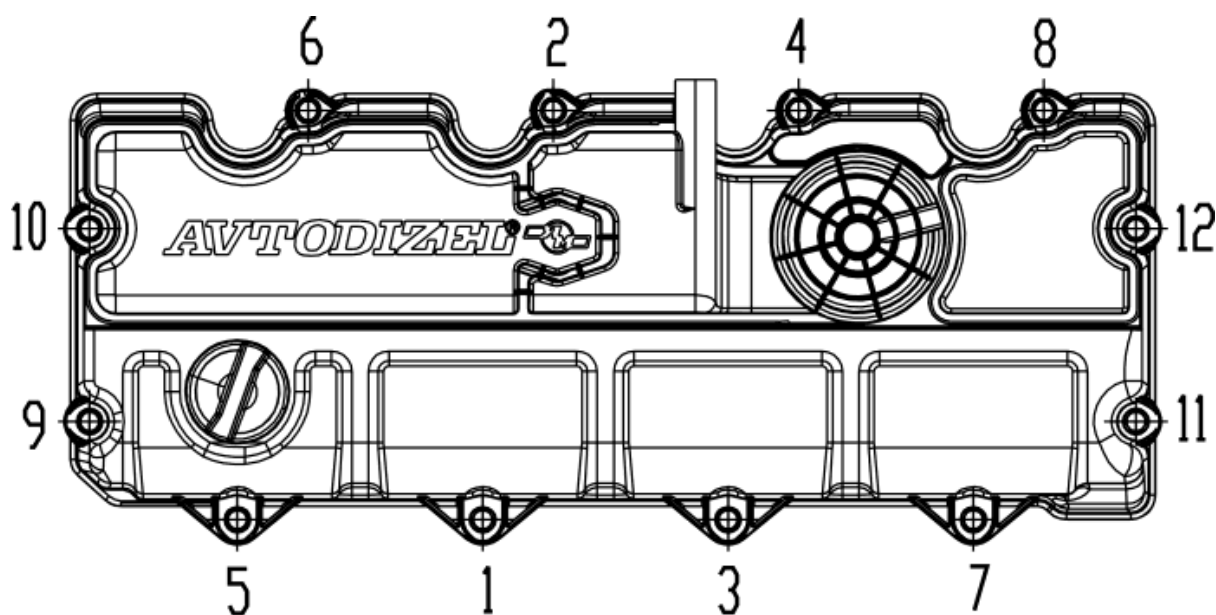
Порядок затяжки болтов крепления крышки головки цилиндров
